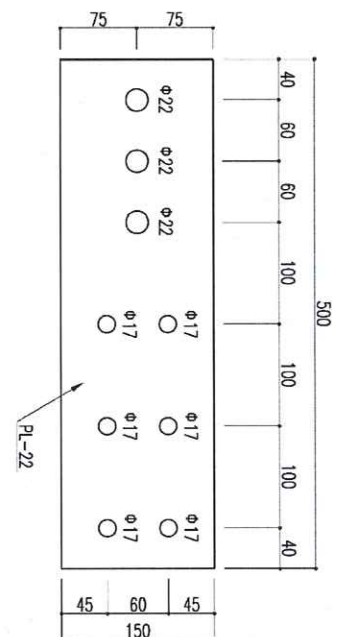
試験法 B 治具詳細図 (2) (単位 : mm)
